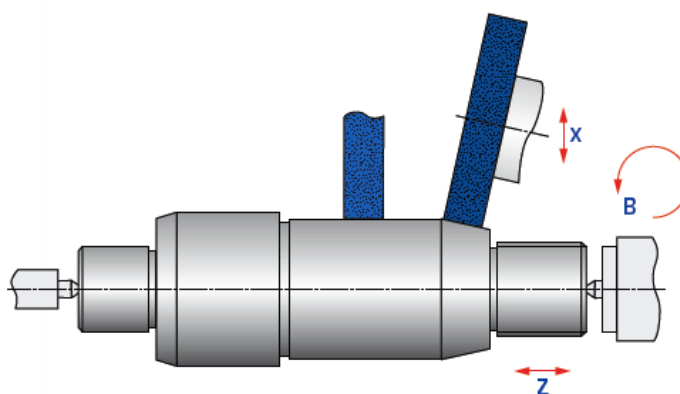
Junker Grindor Silver pro broušení na kulato [14].
